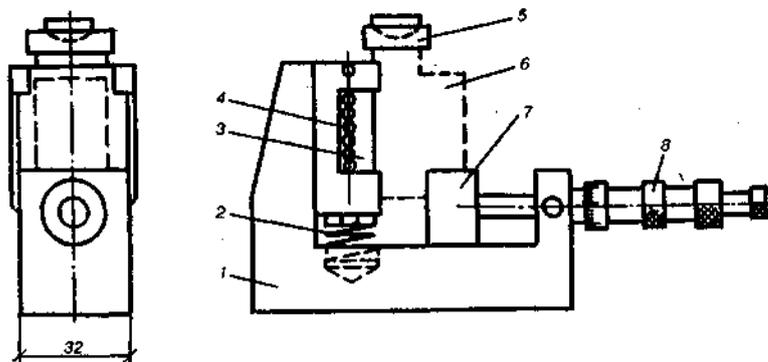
Приспособление для испытания древесины на скалывание вдоль волокон
